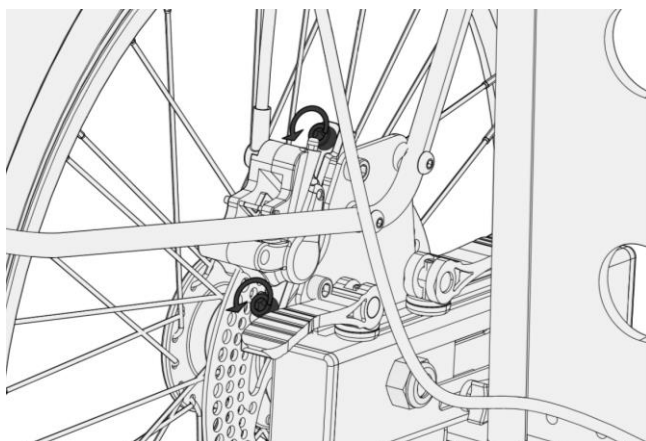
Vue des vis à desserrer pour équilibrer les freins
